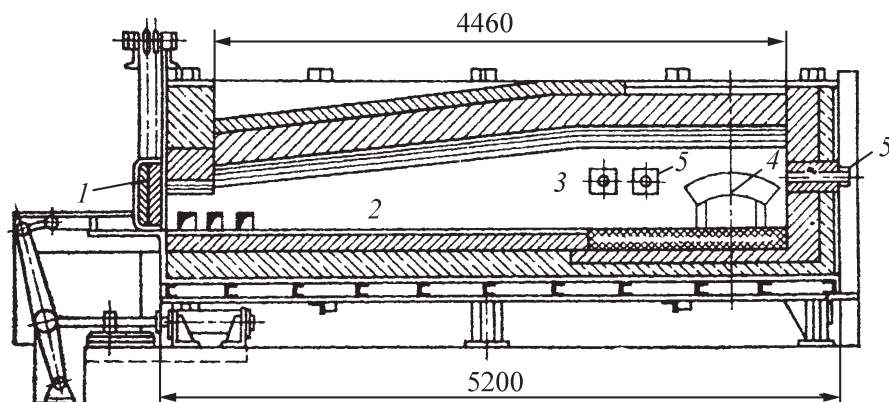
Полуметодическая толкательная печь для нагрева заготовок под штамповку:
